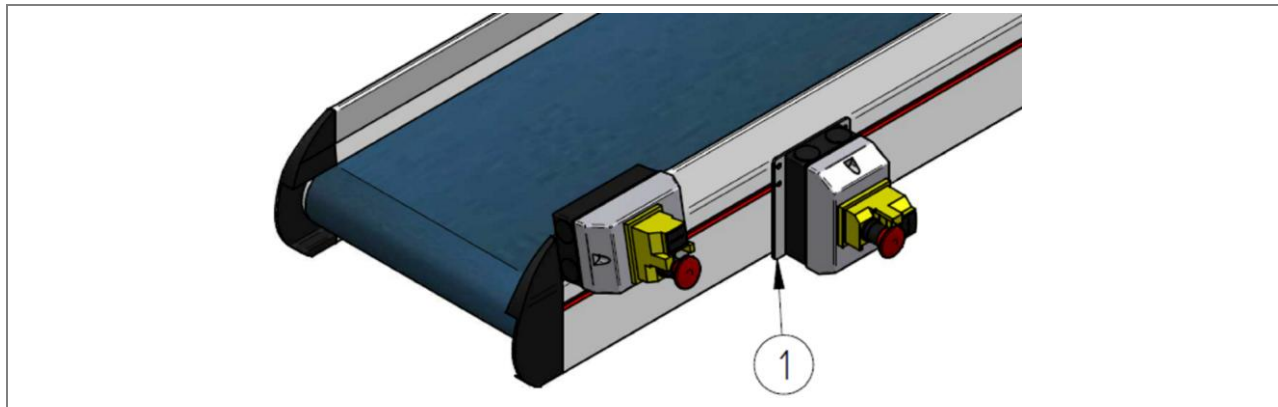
Suportes para interruptor principal — ZZ.982.0104.00
